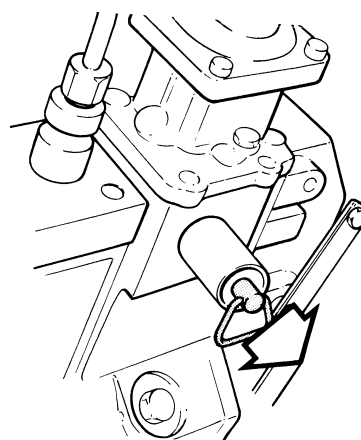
Dispositif de démarrage à froid, TAMD60C
